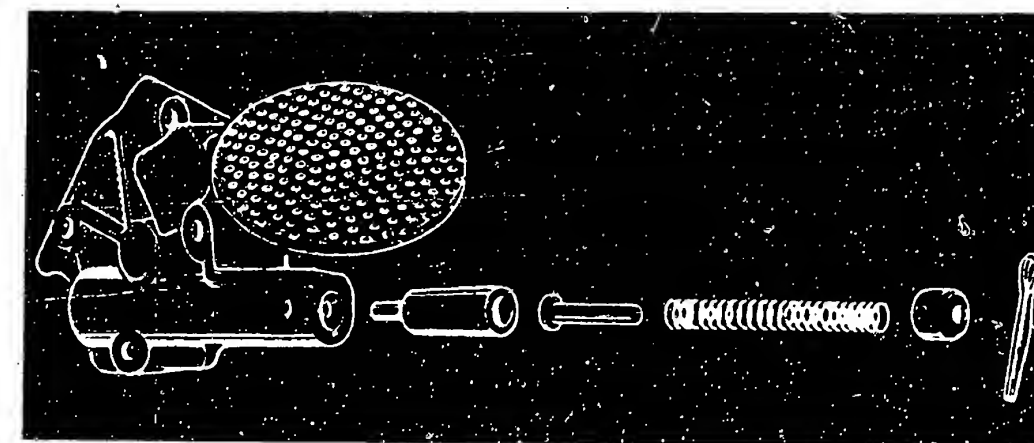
Motor J7T: Einzelteile des Überdruckventils der Ölpumpe.
